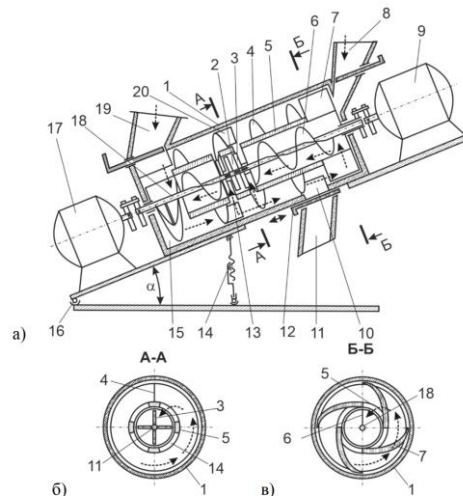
Шнековий змішувач з активним каналом зворотного ходу: а – схема; б – розріз А-А; в – розріз Б-Б, 1 – корпус; 2 – ділянка пересипання; 3 – лопатки; 4 – шнек; 5 – канал зворотнього ходу; 6 – додатковий шнек; 7 – тангенціальні лопатки; 8 – бункер добавок; 9, 17 – приводи; 10 – вивантажувальна частина шнека; 11 – вивантажувальний патрубок; 12 – заслінка; 13 – вікна; 14 – гвинтовий механізм; 15 – завантажувальна частина шнека; 16 – вісь; 18 – вал; 19 – завантажувальний бункер; 20 – плоскі лопатки.
